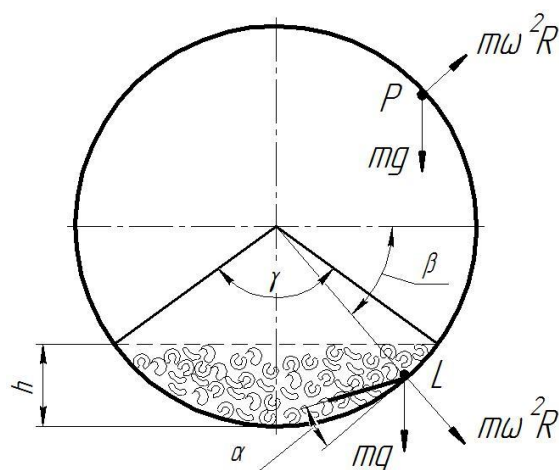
Схема сил, діючих на частинку металеві стружки в поперечному перерізі жолоби шнекового конвеєра з додатковими лопатями
